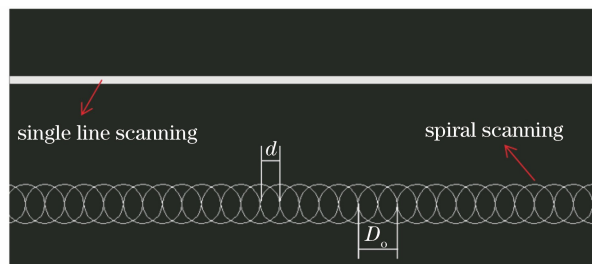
单线刻蚀与螺旋环切刻蚀的 CAD 图
